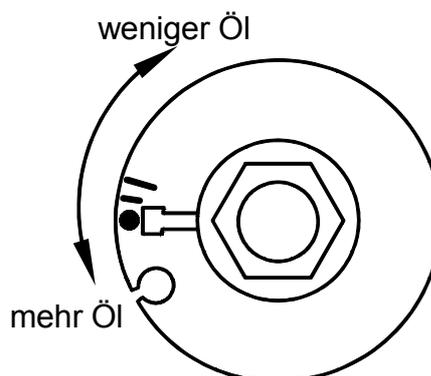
Ansicht der Pumpenscheibe bei Vollgas
